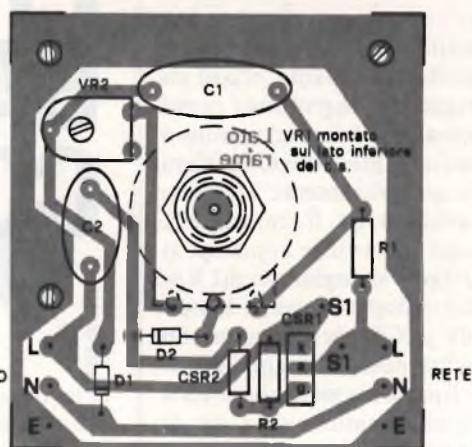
Disposizione dei componenti sulla basetta stampata.
